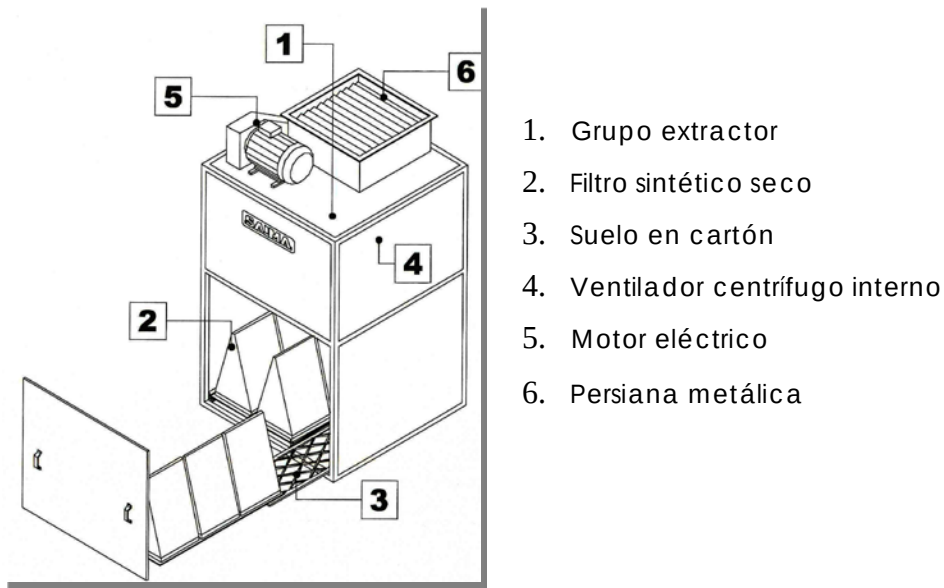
Grupo extractor con filtro seco. Fuente: Manual de uso y mantenimiento SPANESI. Descripción técnica. Cabinas de pintura. pag. 21
